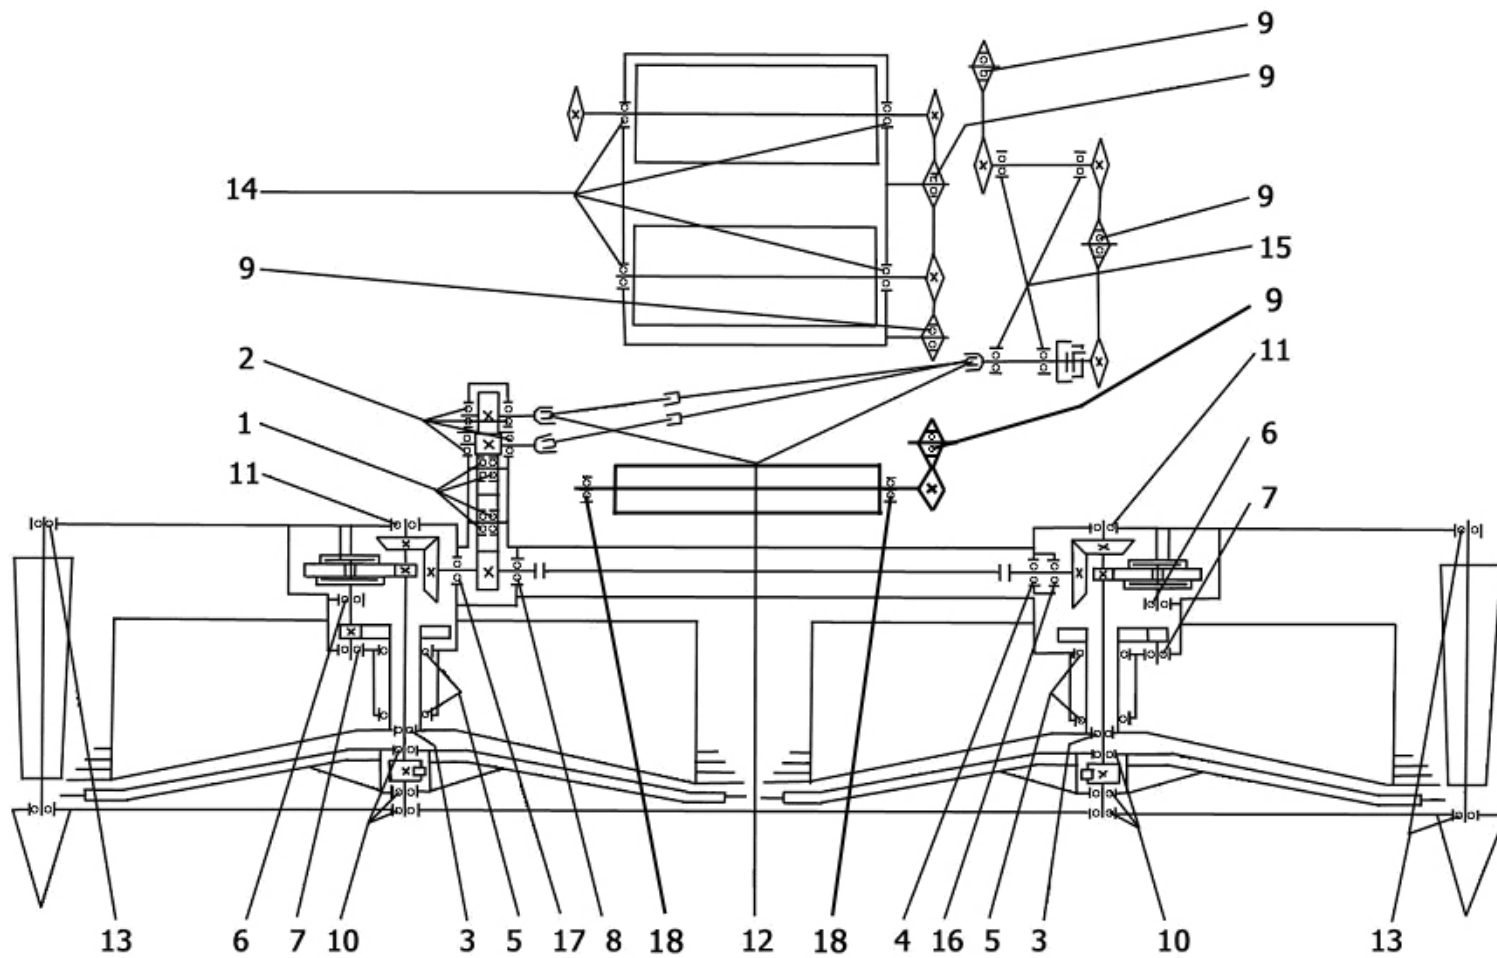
Схема расположения подшипников жатки роторной ЖР-4000 к комбайну «Дон-680»
